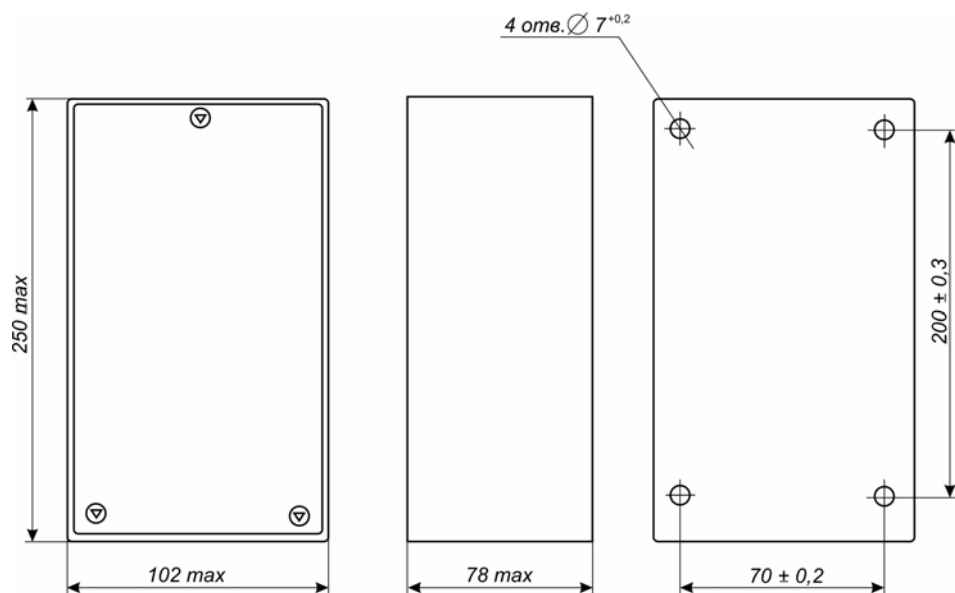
Габаритные и присоединительные размеры паркового переговорного устройства ППУ.М2
